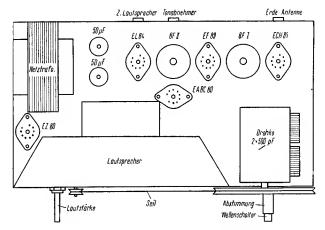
Aufbauschema für das Chassis des 6-Kreis-Superhets
